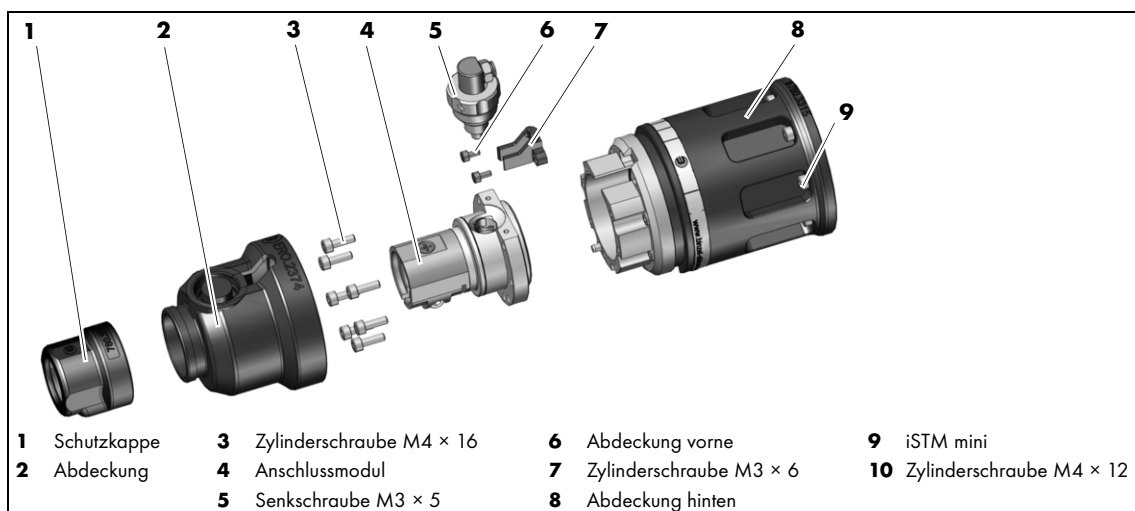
Lieferumfang iSTM mini für ABIROB® G mit Wire-Brake
